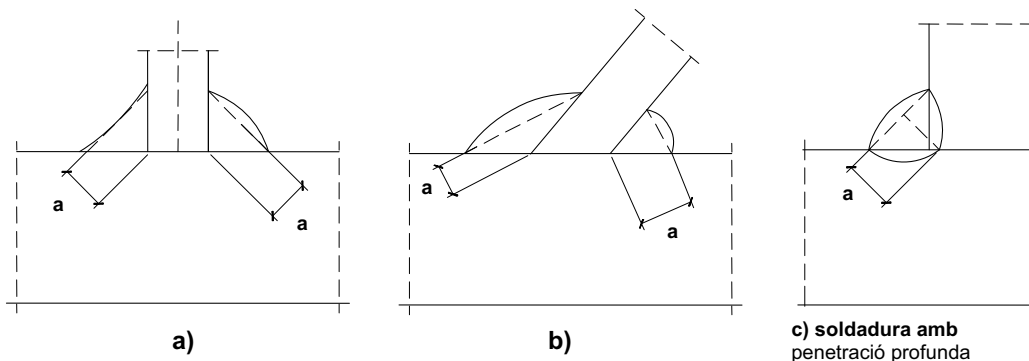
Soldadura en angle. Gruix de coll
